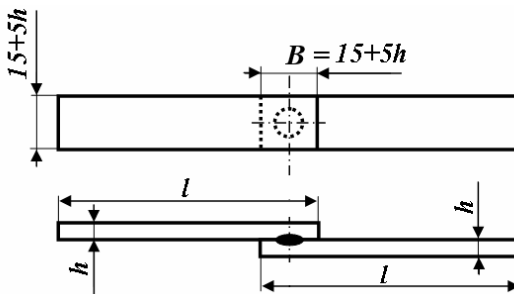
Вид нахлестки сварного соединения, выполненного контактной точечной сваркой
